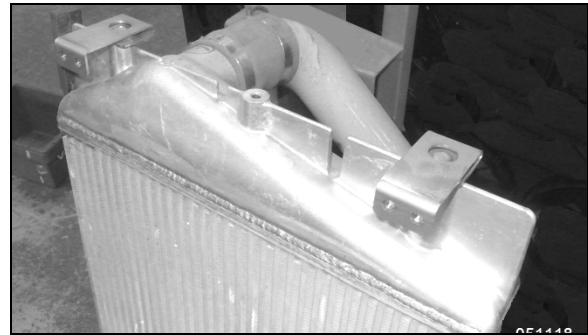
SOPORTES & TUBO SUPERIORES DEL CAC
